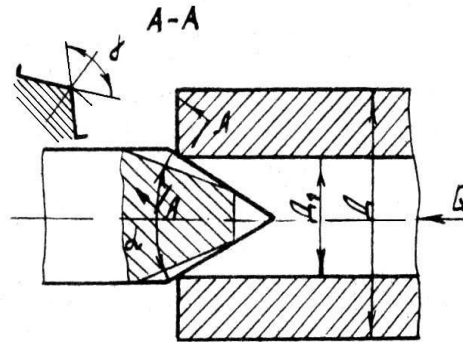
Розрахункова схема установки заготовки на рифлений повідковий центр
